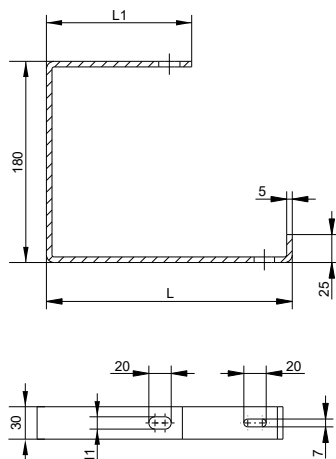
Подвес С-образный / Figure B.1 – C-shaped suspension
